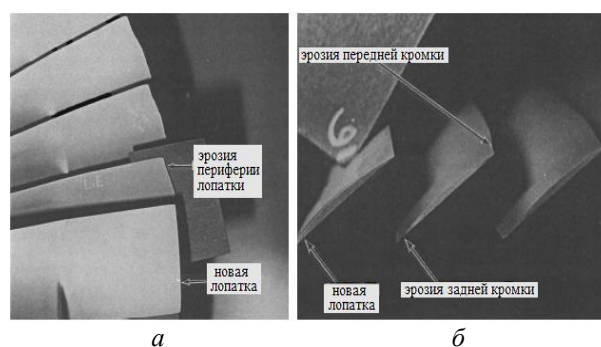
Пример износа рабочих лопаток компрессора двигателя F 100-PW-100:
